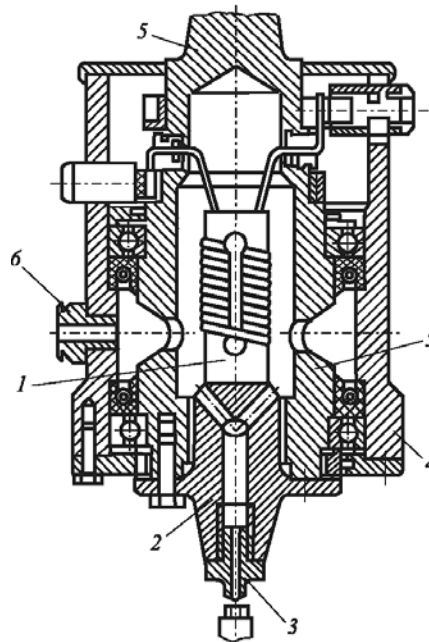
Устройство вращающейся акустической головки с магнитострикционным преобразователем
